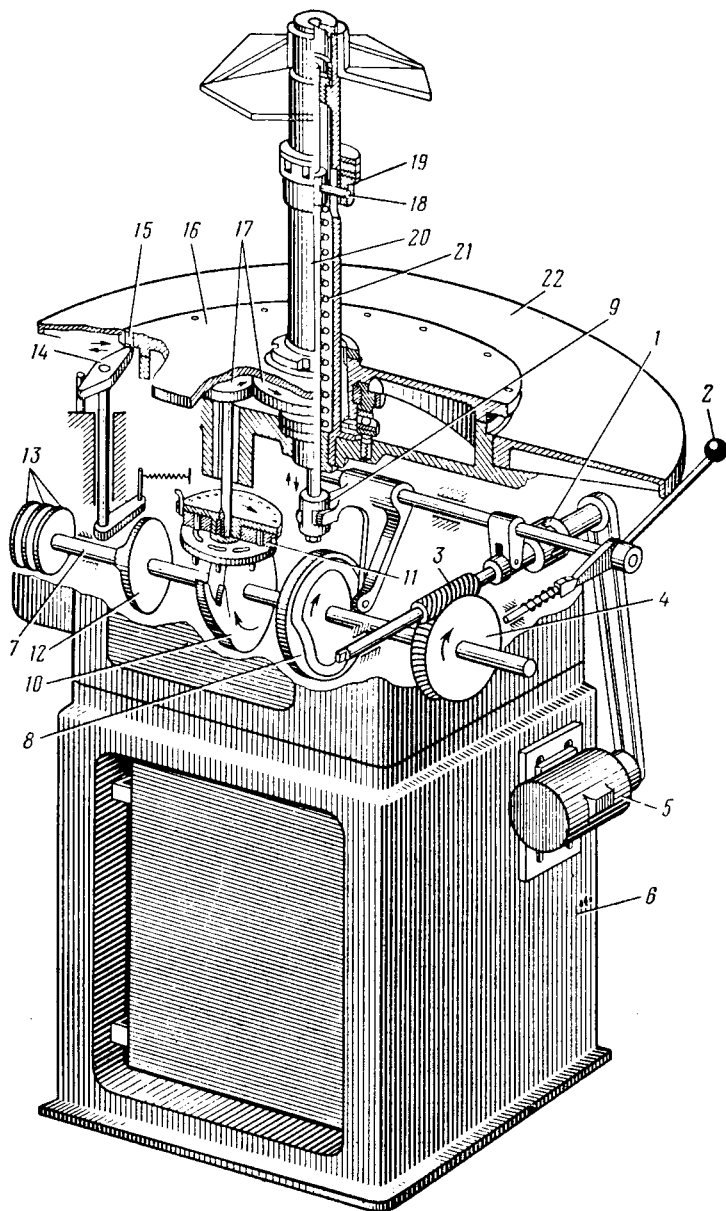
Схема агрегатного станка для сборки с круговым движением стола
